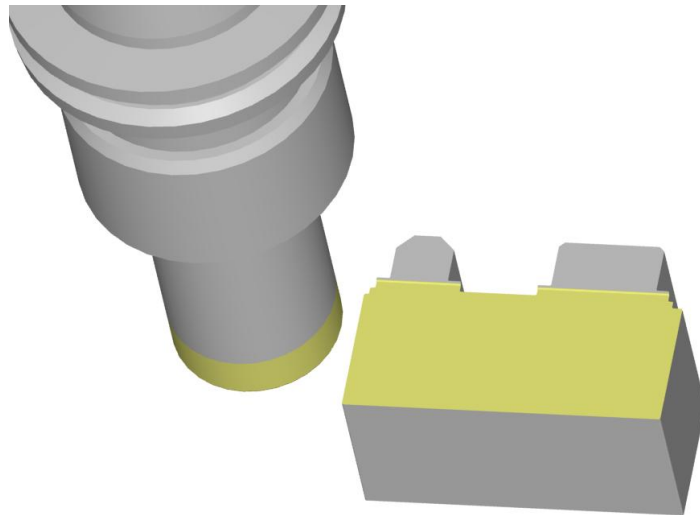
CNC programování 1. upnutí v EdgeCAM 2011R1
